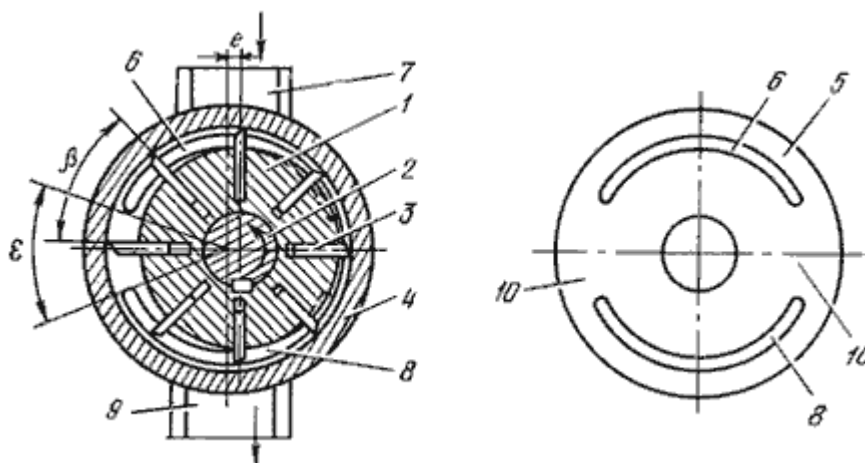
Схема пластинчатого насоса однократного действия: 1 - ротор; 2 - приводной вал; 3 - пластины; 4 - статор; 5 - распределительный диск; 6, 8 - окна; 7 - гидролиния всасывания; 9 - гидролиния нагнетания
